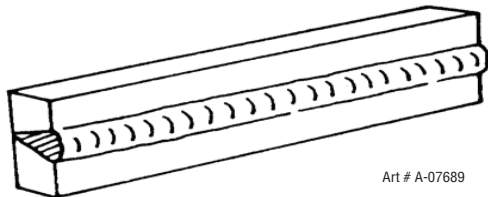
Position horizontale, soudure bout à bout
